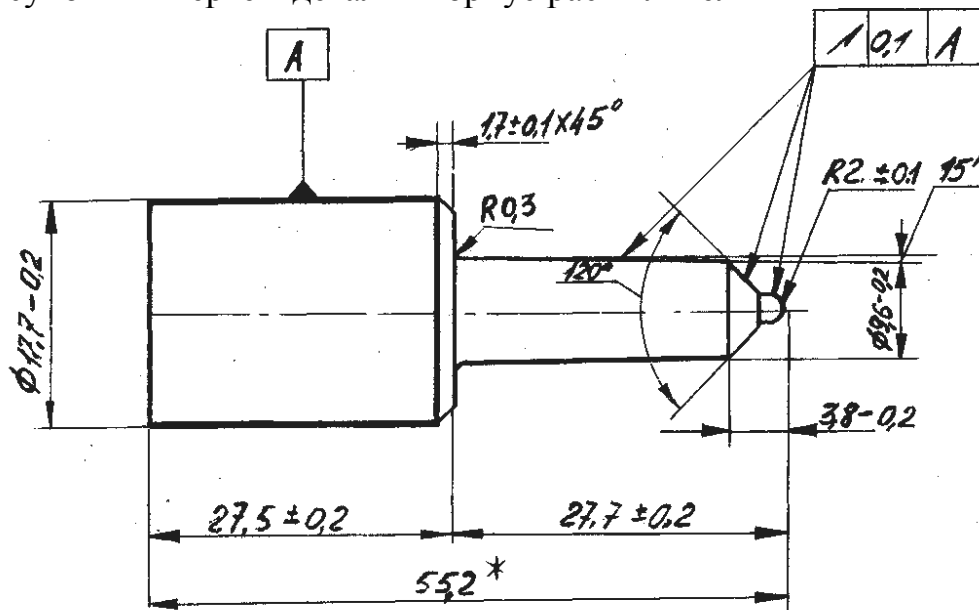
Чертеж поковки детали «корпус распылителя»
